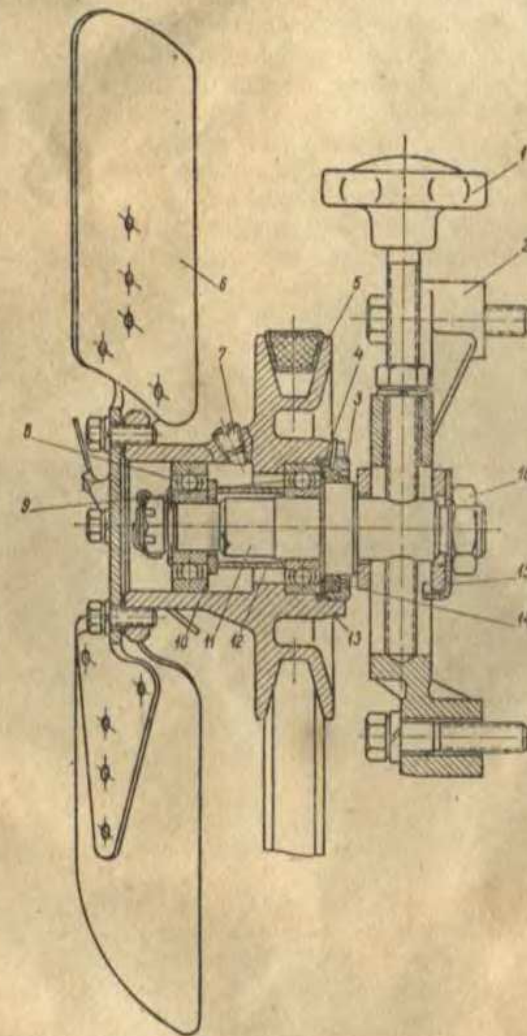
Вентилятор двигателей ЯАЗ-М204:
